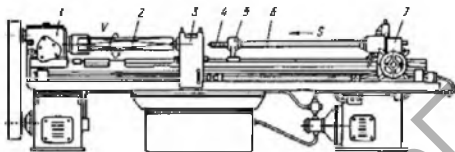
Горизонтально-сверлильный станок для глубокого сверления вращающихся деталей
